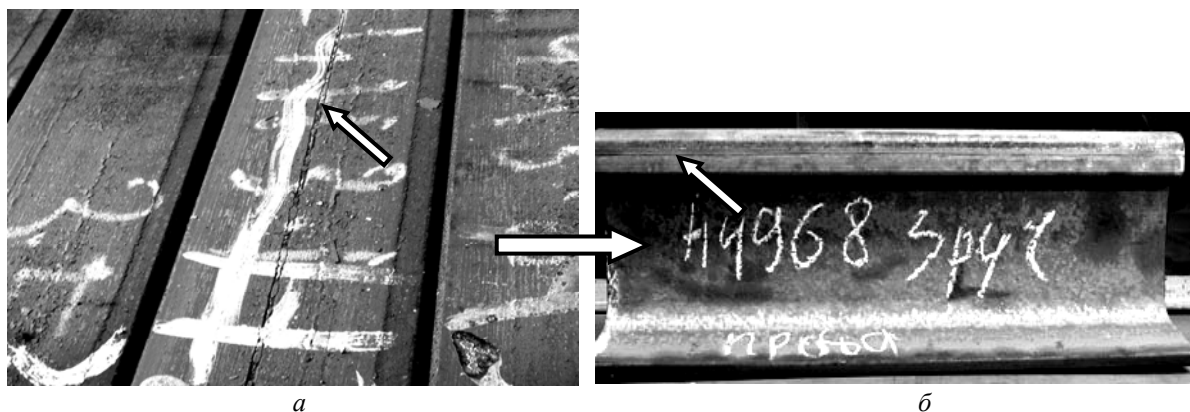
Пример наследования дефекта металлопроката: *а* – заготовки с трещиной, заполненной частично металлом и шлаковыми включениями; *б* – раскатанная трещина на поверхности рельса
